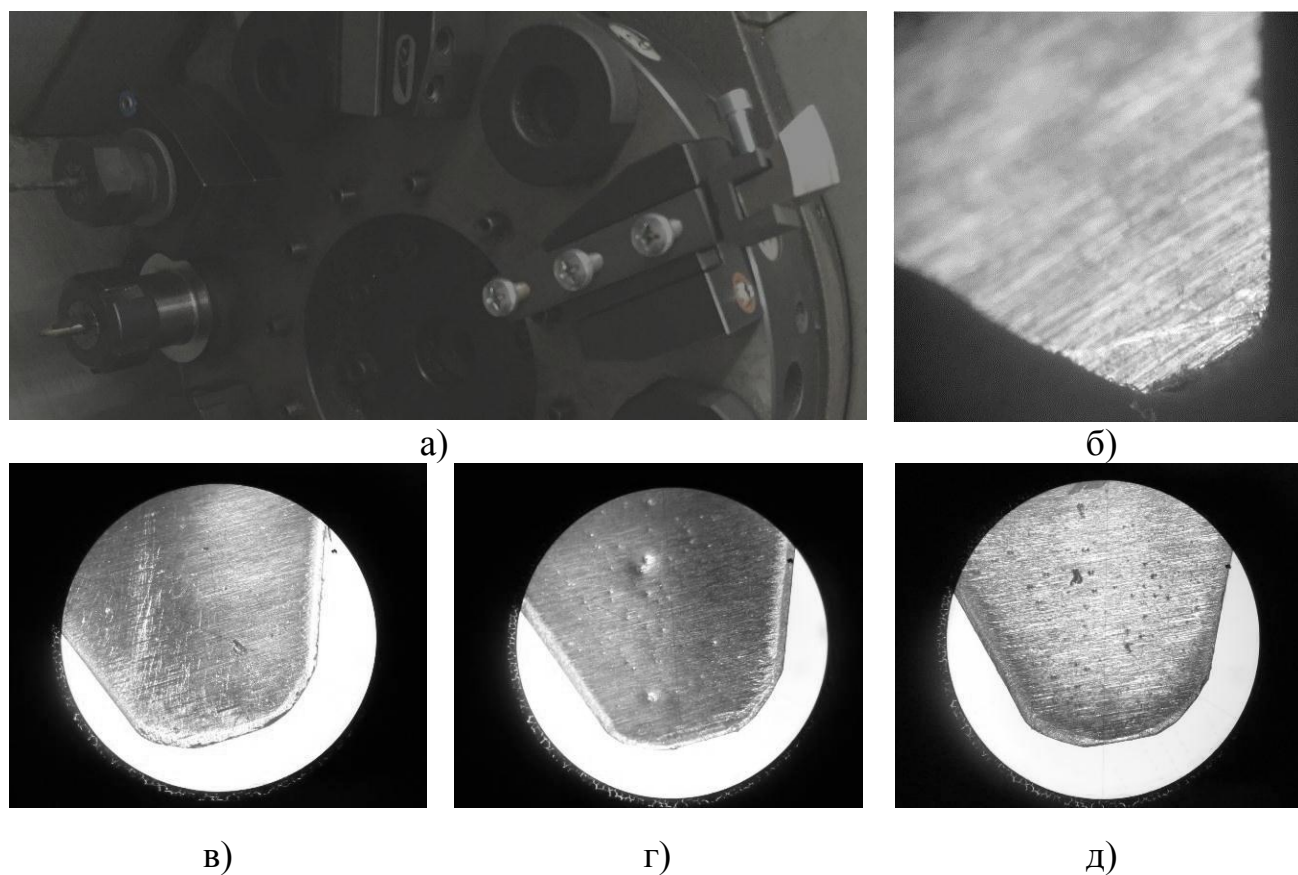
Износ режущих поверхностей зубчатых реек экспериментальной червячной фрезы:
